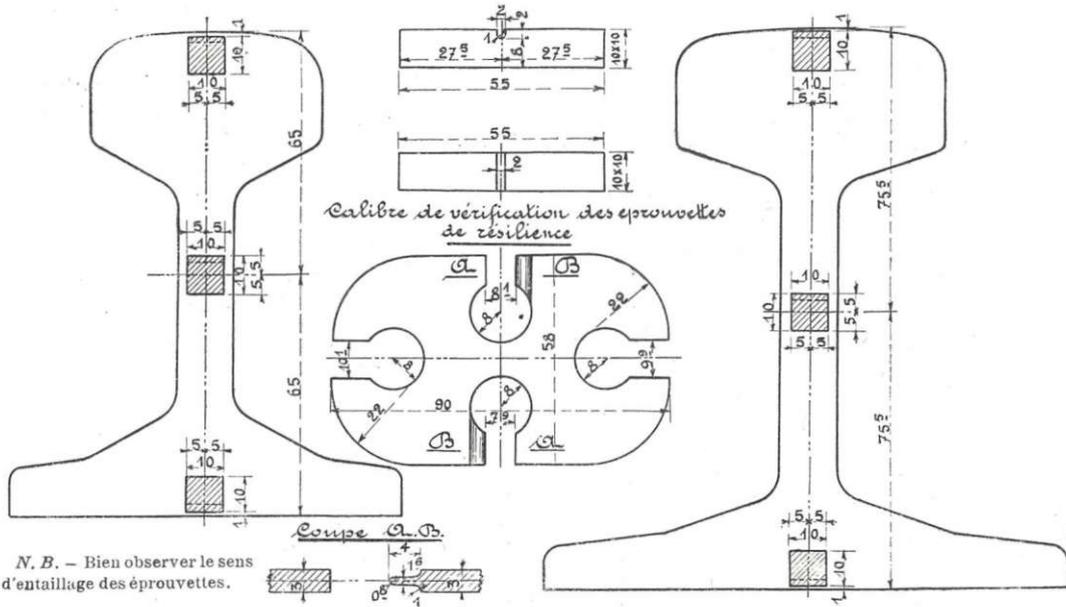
à 49. — Emplacement des éprouvettes pour épreuve de résilience.
